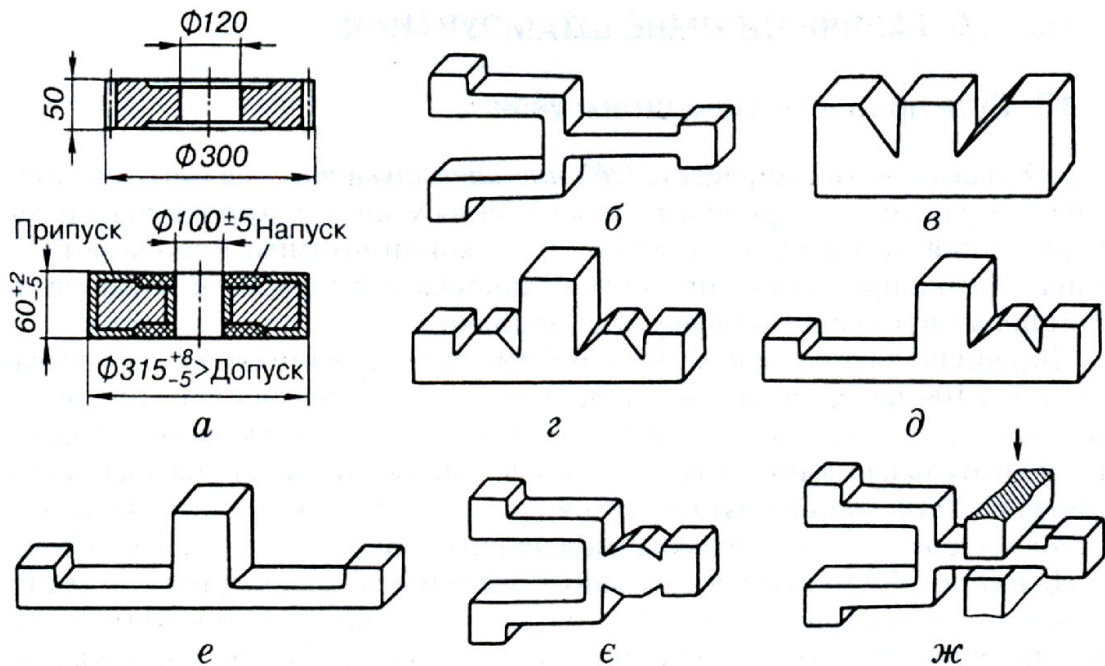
Креслення поковки шестерні і схеми технологічного процесу кування важеля з вилкою
